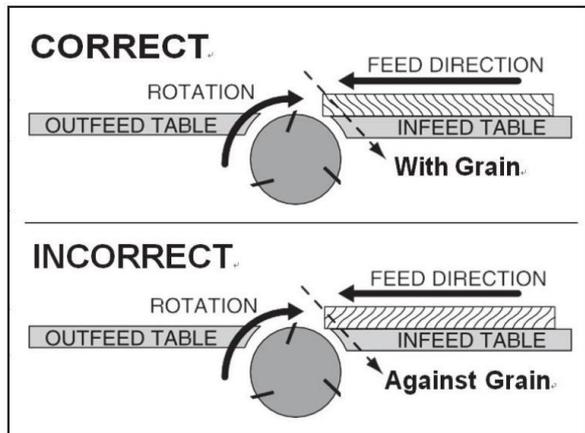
Правильное положение волокна заготовки по отношению к режущему валу.
